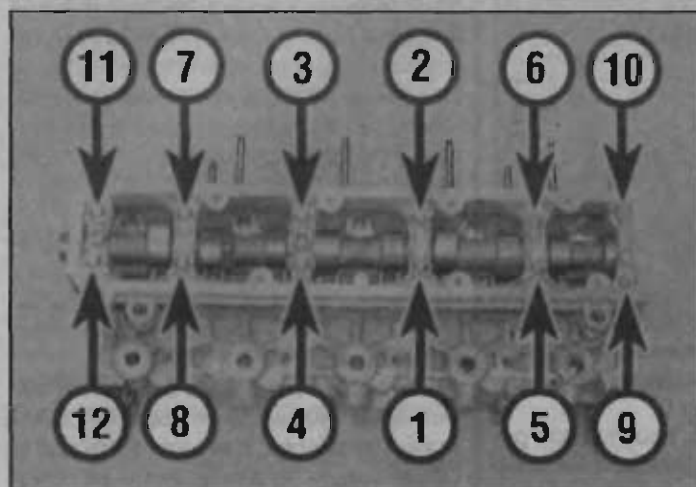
Последовательность затягивания болтов крепления корпуса подшипников распределительного вала
